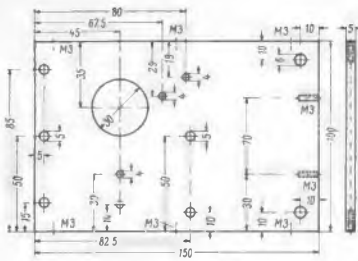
Obere Grundplatte, Aluminium 5 mm
